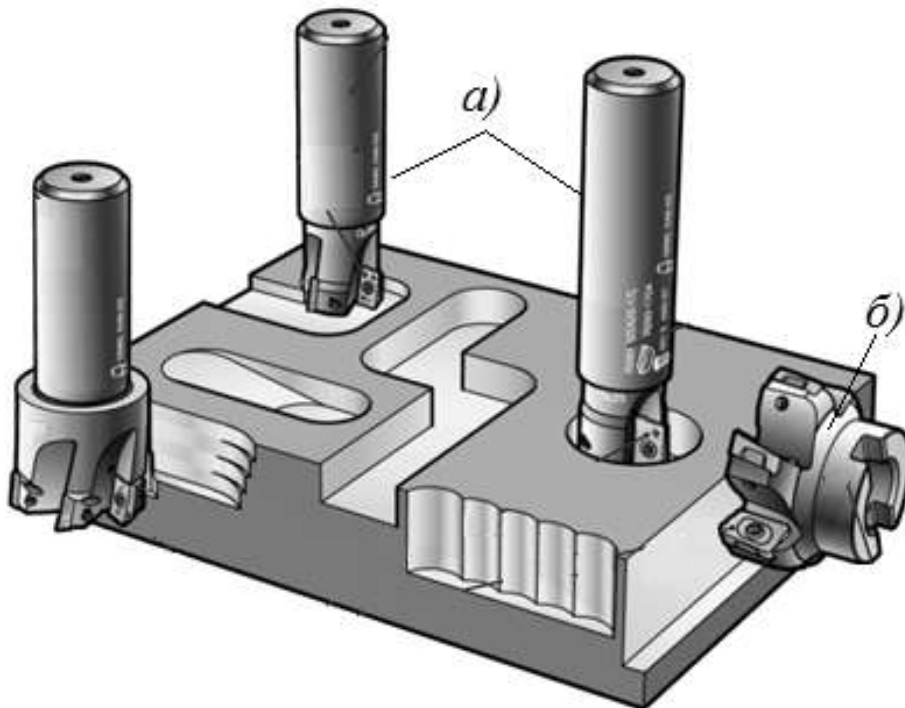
Обробка різних поверхонь циліндричними кінцевими (а) та торцевими (б) фрезами
